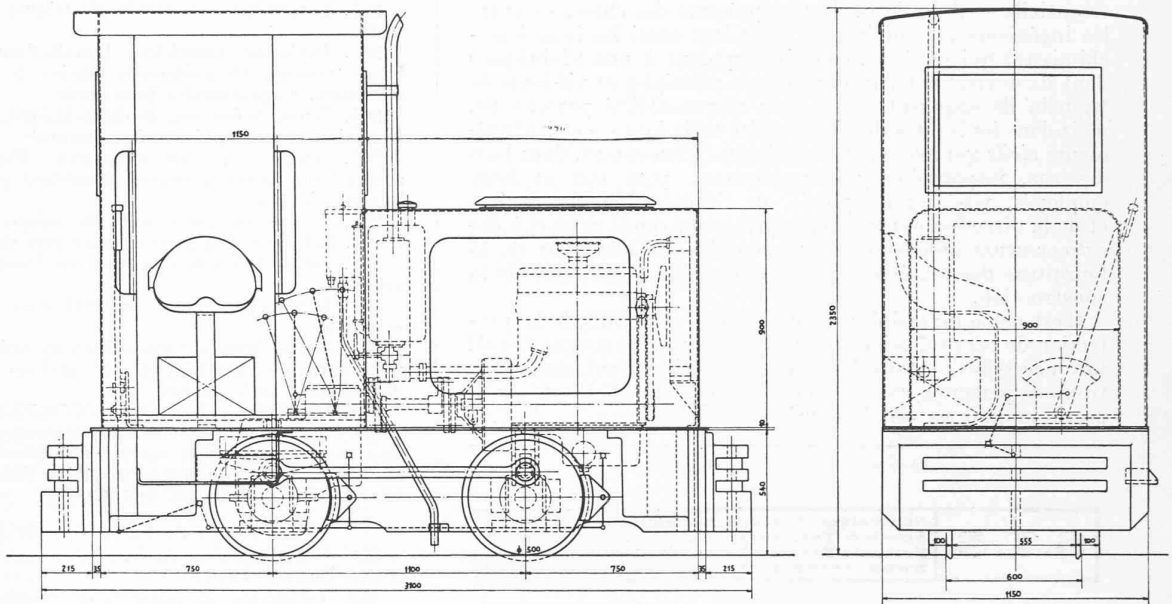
Croquis-type de la locomotive Diesel-mécanique de 25 CV.
